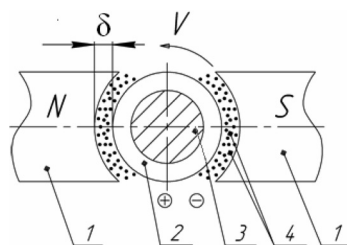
Схема МАО: 1 – полусферические наконечники; 2 – обрабатываемая заготовка; 3 – ферромагнитная оправка; 4 – ФАП; δ – рабочий зазор; V – скорость вращения заготовки
